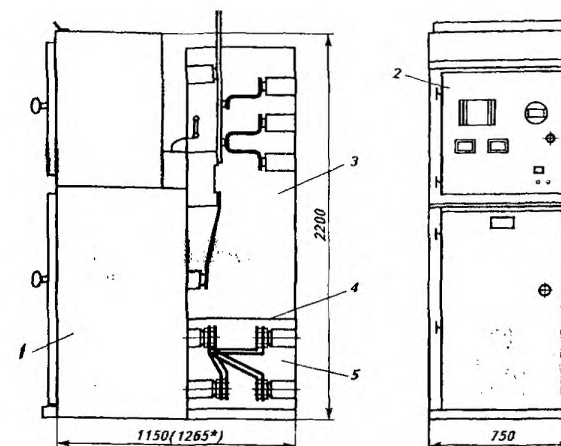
Шкафы КРУ серий К-104 и К-104МС1 с выключателями и шинными вводами сверху
